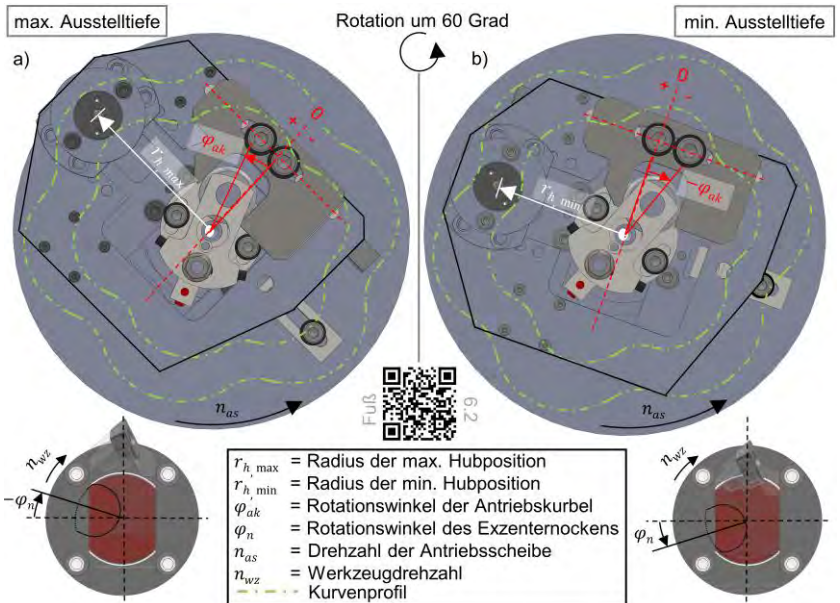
Skizzen zur Bewegungsmechanik des AK-UR-Antriebs mit Bezug zum Werkzeug
